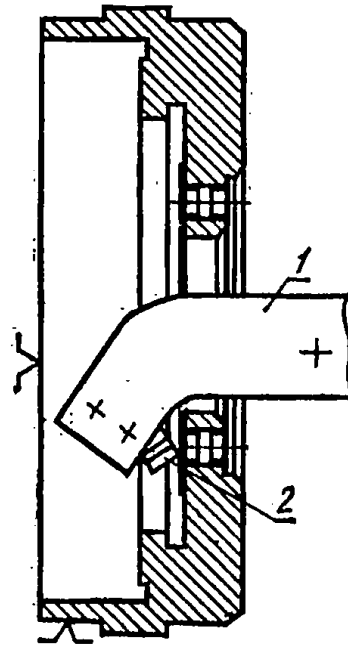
Схема обработки выступающих сварочных швов со стороны закрытого торца:
